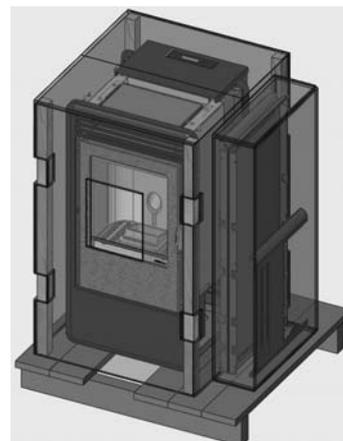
Imballo stufa + fianchi in acciaio stufa Kaika
